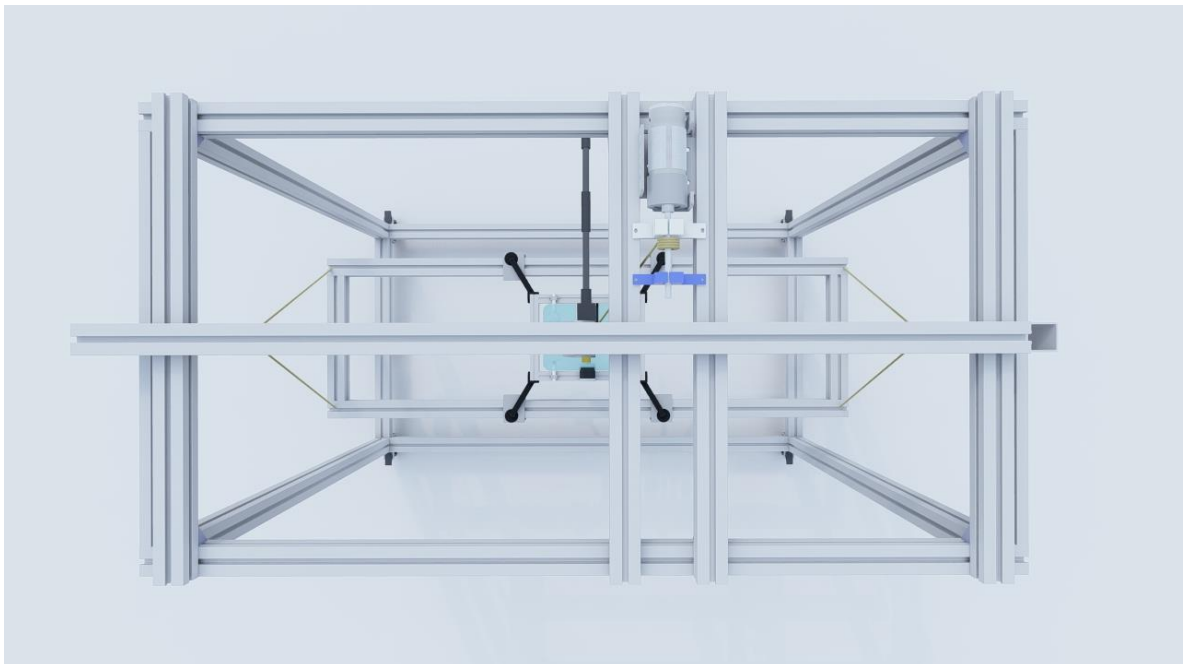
Vista superior de diseño CAD - Dispositivo de limpieza.
